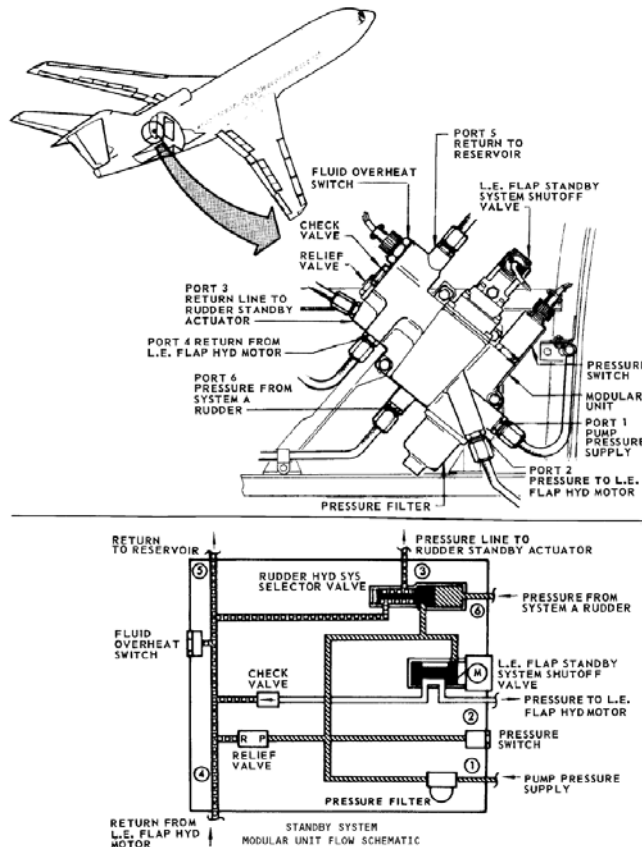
Unidad modular (modular unit) (Fuente: B727-AMM)
